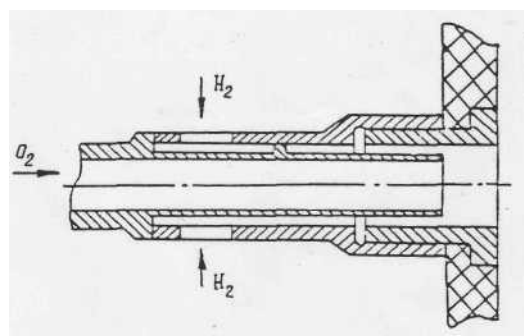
Смесительный элемент головки двигателя АЕСЕ
